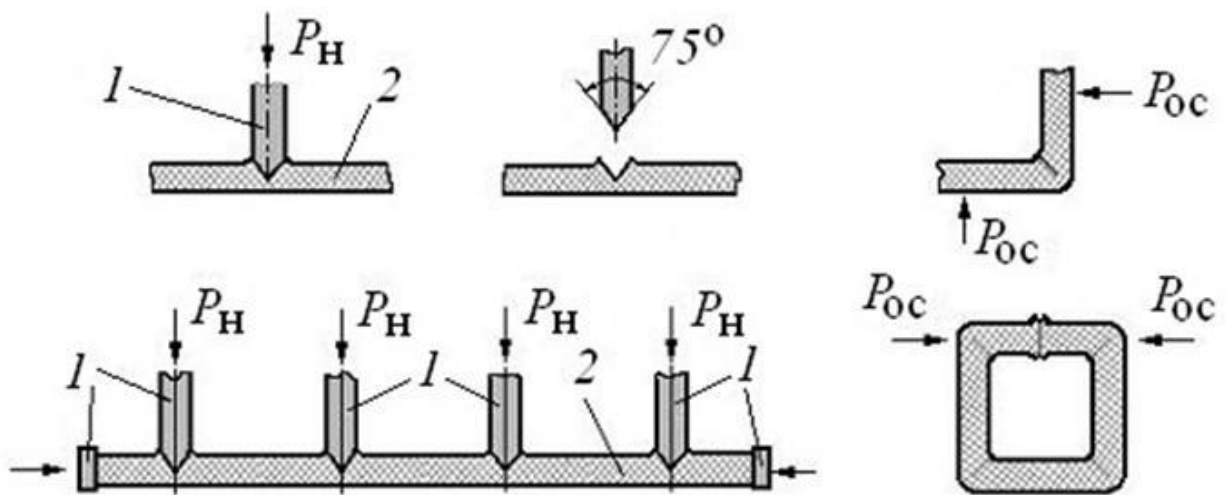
Схема зварювання з перегином: 1 - нагрівальний інструмент; 2- лист термопласта.
